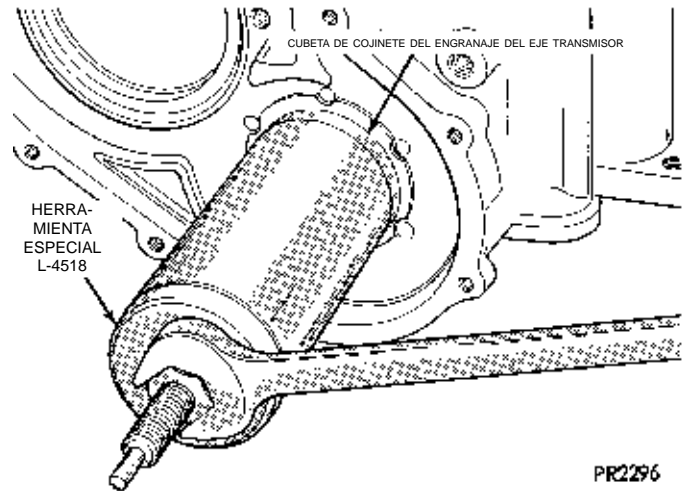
Desmontaje de la cubeta de cojinete del engranaje del eje transmisor
